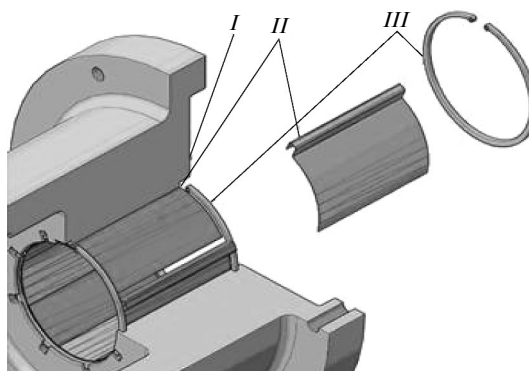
Лепестковый опорный газодинамический подшипник. *I* — корпус; *II* — лепестки подшипника; *III* — фиксатор подшипника
